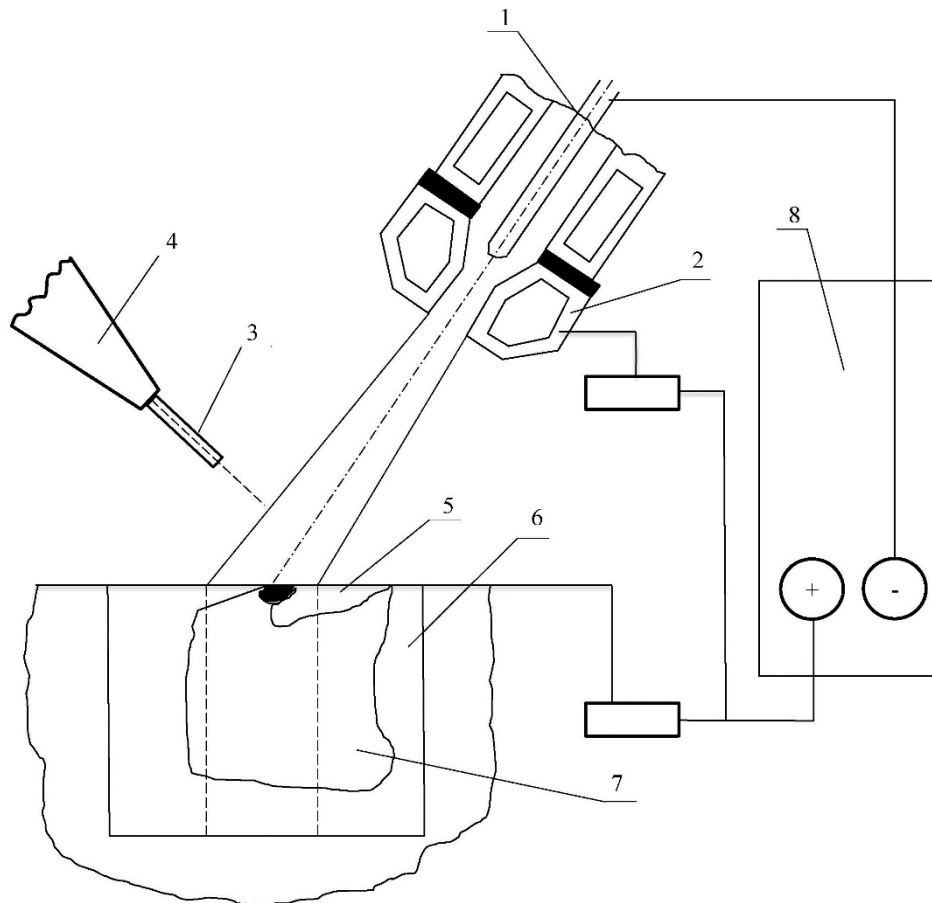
Принципова схема наплавлення зубів пил прутками із литих твердих сплавів: 1 – електрод; 2 – сопло; 3 – наплавочний пруток; 4 – механізм подачі прутка; 5 – плашки з лункою; 6 – корпус для кріплення плашок з водоохолодженням; 7 – пила; 8 – джерело живлення
